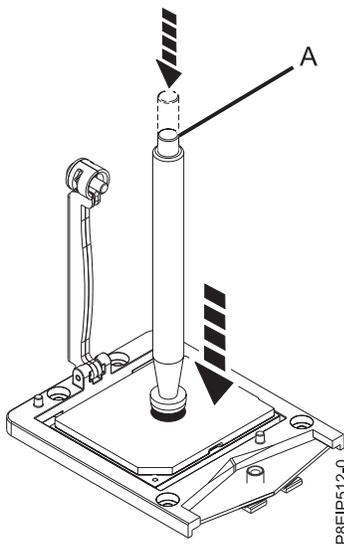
Ausbauwerkzeug auf das Systemprozessormodul herabsenken
